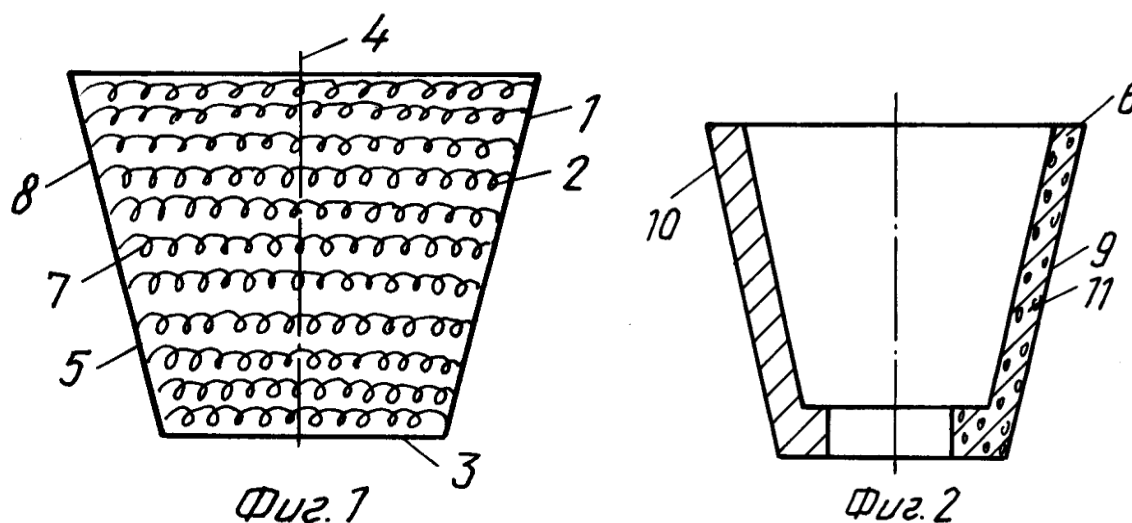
Проволочный фильтр (вид с боку и сверху)
